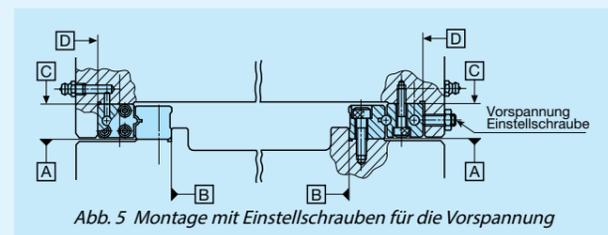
Montage mit Einstellschrauben für die Vorspannung
